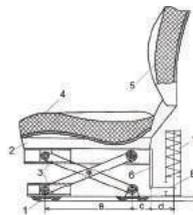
б. Общий вид подвески сиденья с направляющим механизмом типа «ножницы».
